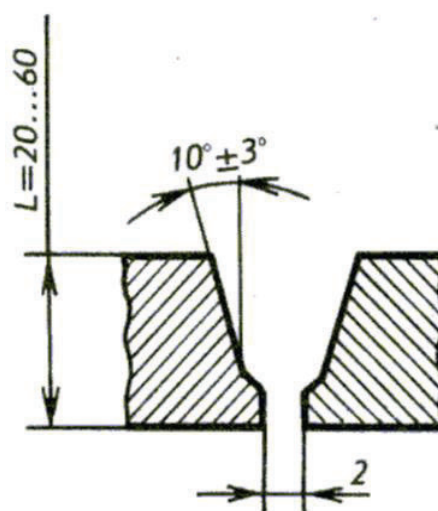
Підготовка кромки металу товщиною понад 20 мм до зварювання
